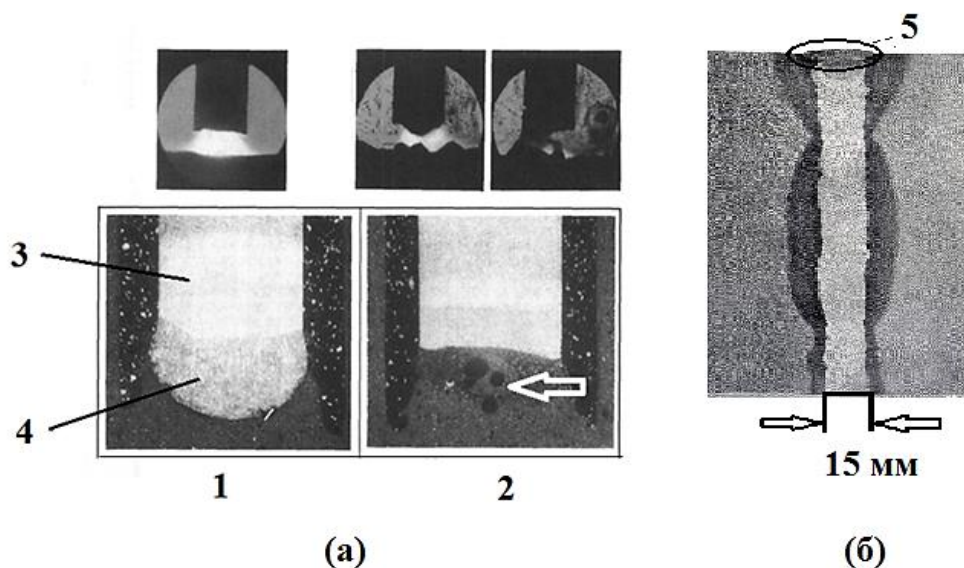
Визуализация шлаковой ванны и наплавленного металла при сварке рельса электродами (а) с основным покрытием (поз. 1) и рутиловым (поз. 2) и поперечный темплет макроструктуры рельсового стыка, сваренный по способу Enclosed arc welding process (б):
